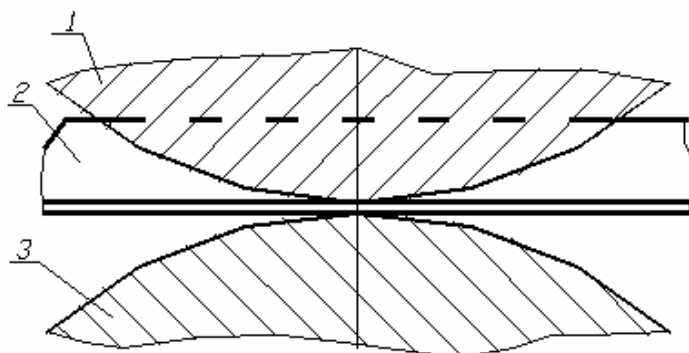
Схема волочения в роликовой фильере: 1 – верхний ролик; 2 – профилированная заготовка; 3 – нижний ролик
